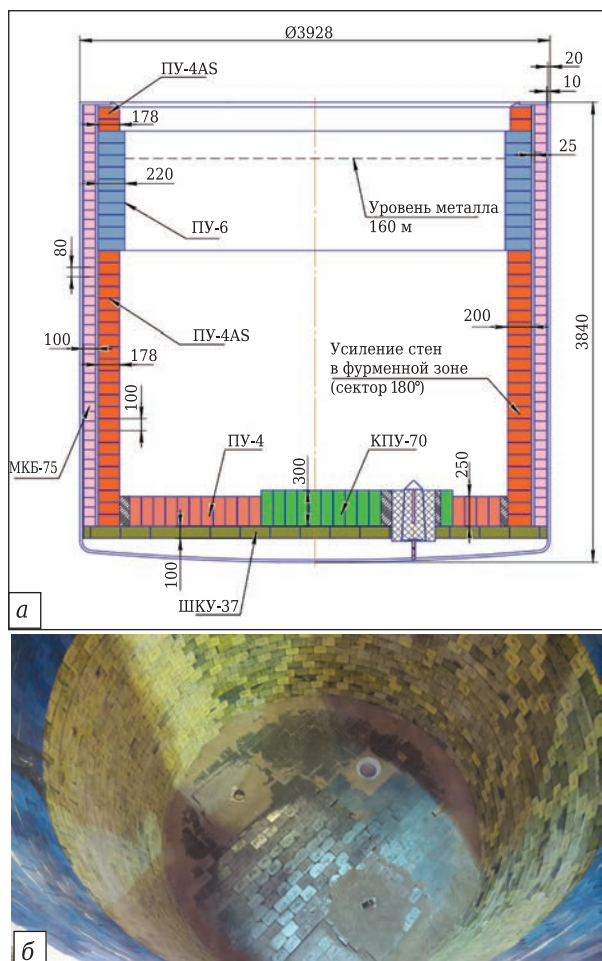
Условная схема (а) и внешний вид футеровки 160-т сталеразливочного ковша ЭСПЦ АО ОЭМК (б)
